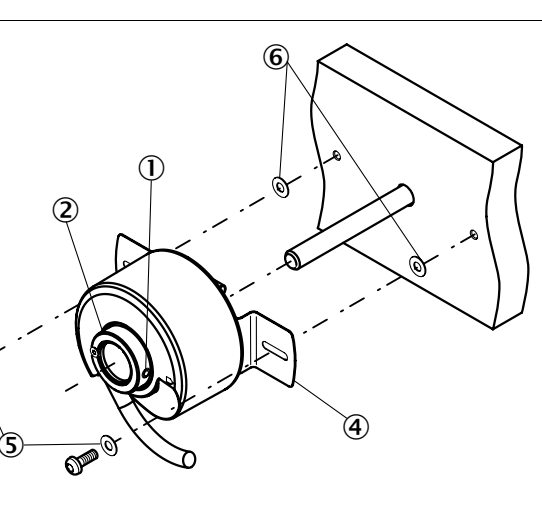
Anbau mit axialer Passstiftmontage Variante C
